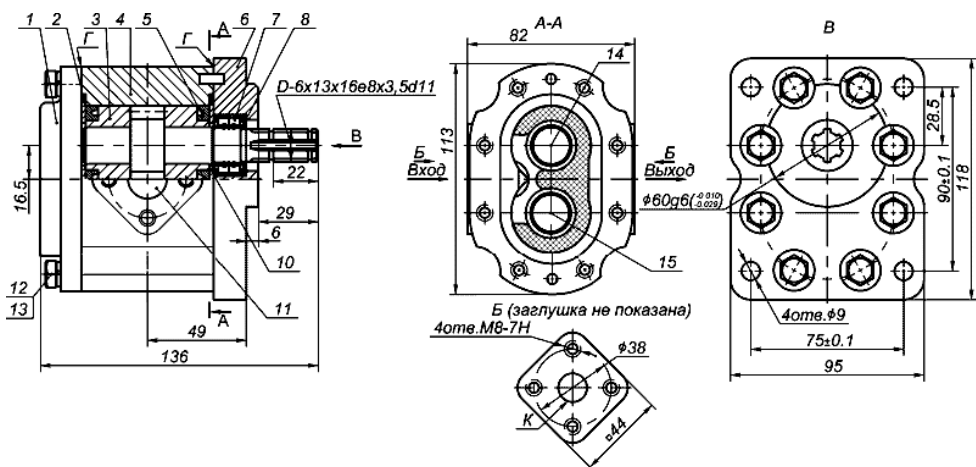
Чертеж общего вида насоса типа НШ6Е-3: 1-крышка задняя; 2 - кольцо уплотнительное; 3 – подшипник; 4 – корпус; 5 – манжета фигурная; 6 - крышка передняя; 7 – манжета; 8 – кольцо опорное; 9 – штифт; 10 – пластина; 11 – канал; 12 - болт; 13 -шайба; 14 - шестерня ведущая; 15 – шестерня ведомая.
